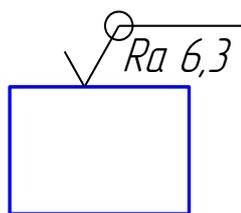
Обозначение шероховатости поверхностей, образующих контур [21]
